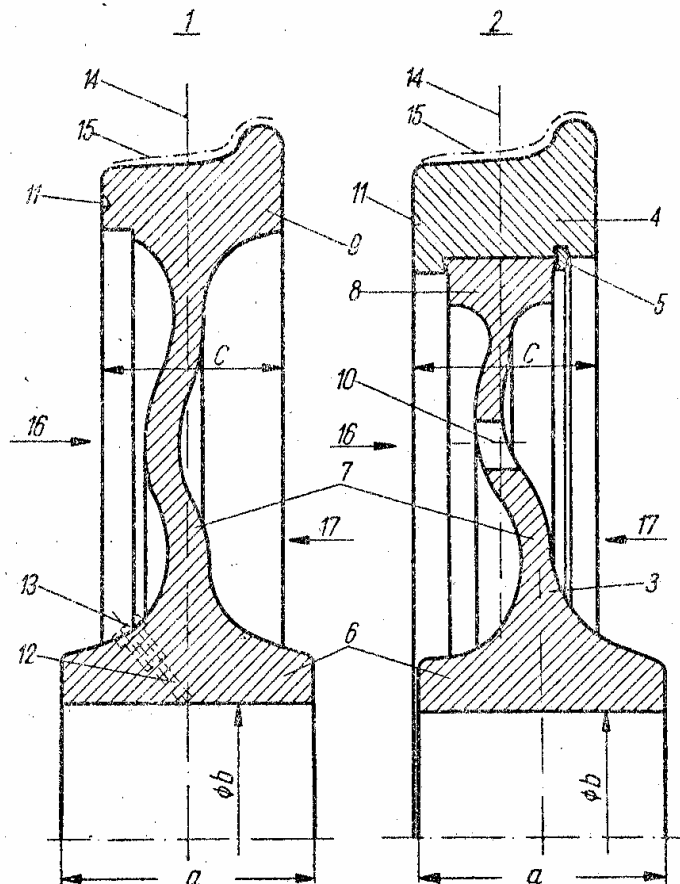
Przekrój zestawu kołowego obręczowanego i bezobraczowego.
